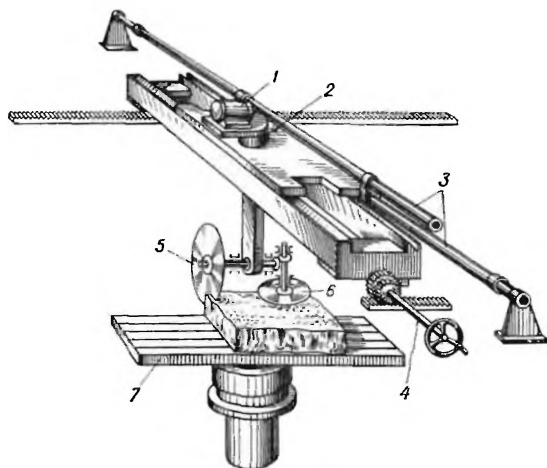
Кинематическая схема фрезерно-окантовочного мостового станка модели СМР-15:
